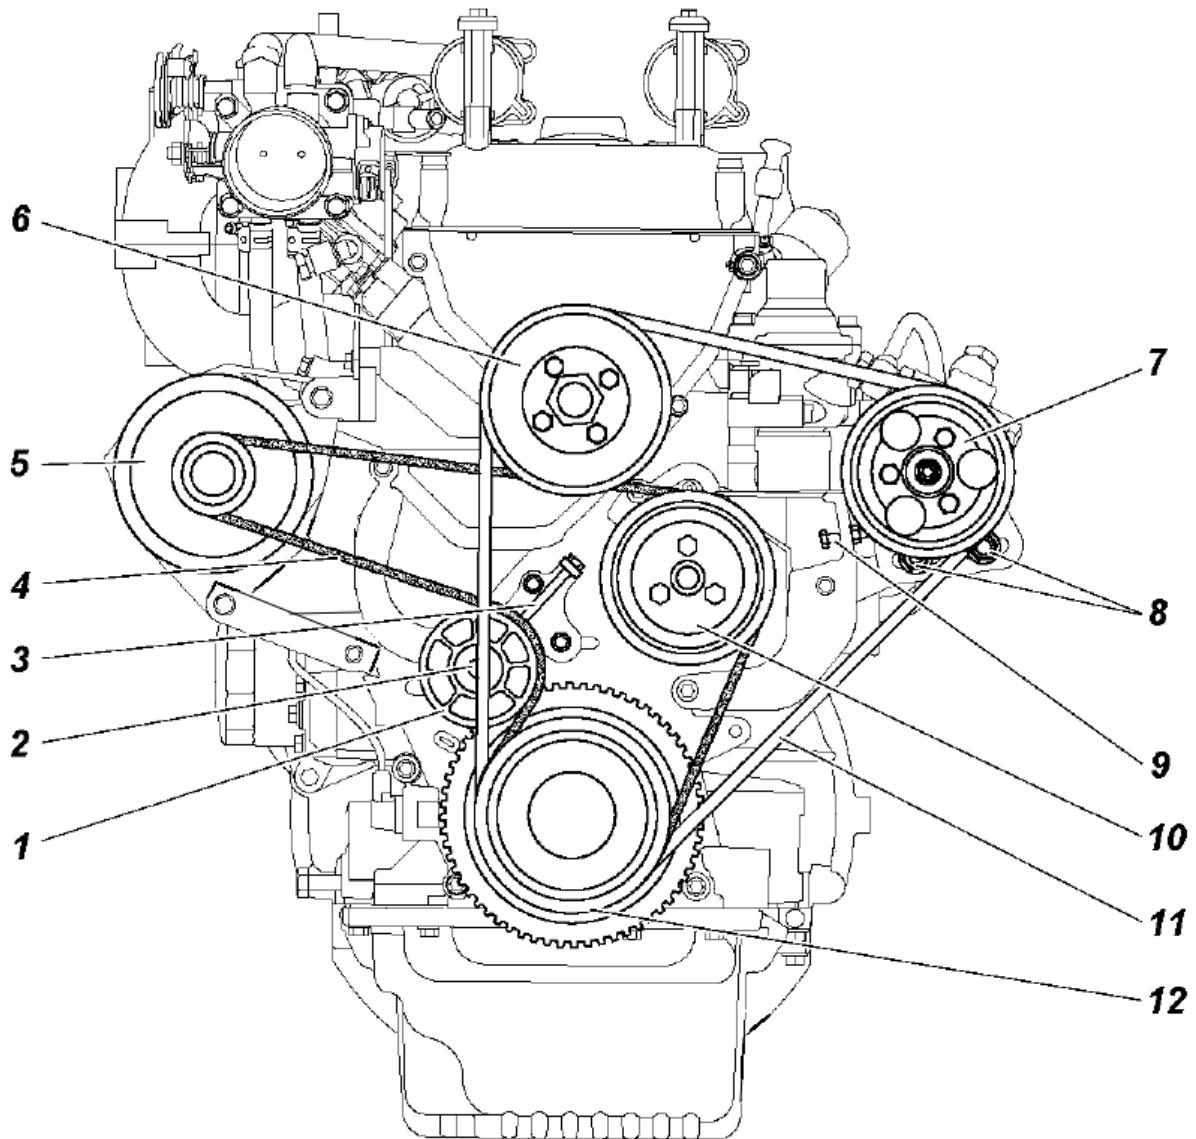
Схема привода агрегатов двигателя с насосом ГУР:
